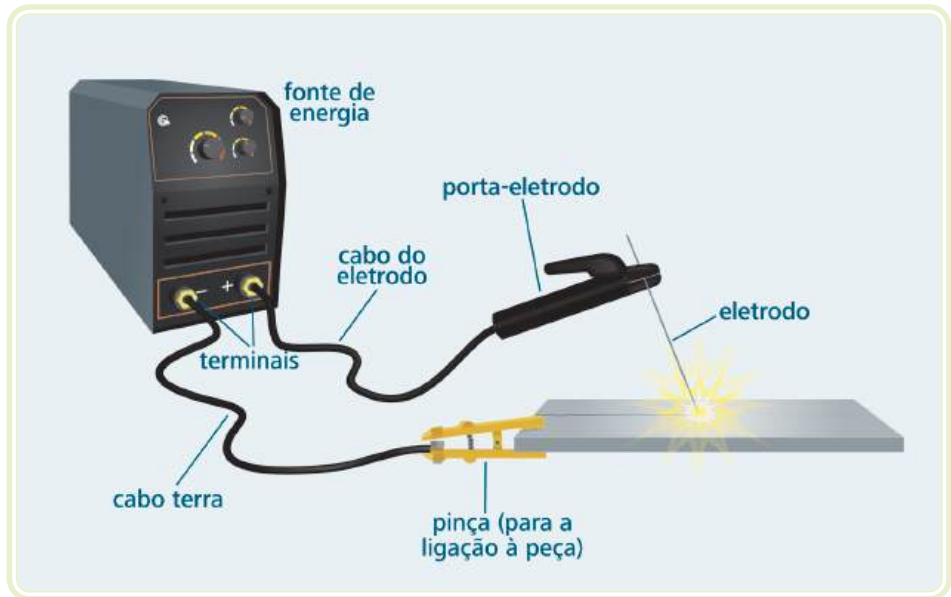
Bancada que mostra o equipamento para soldagem através do processo de soldagem eletrodo revestido
